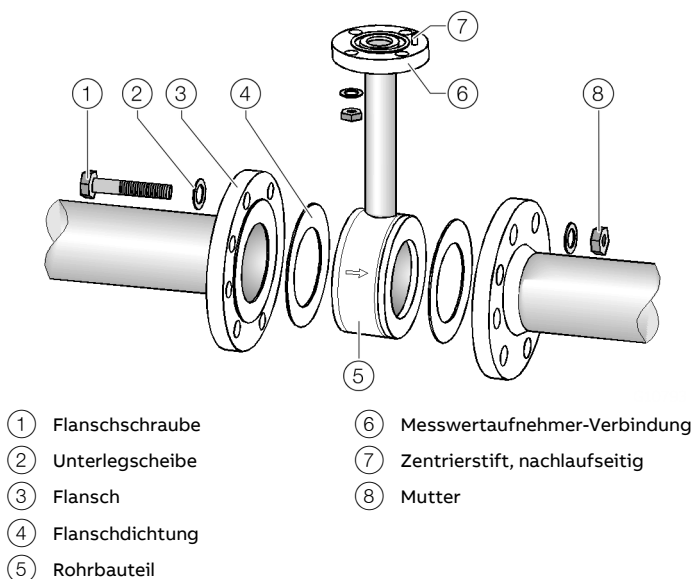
Montage Rohrbauteil (Beispiel, Zwischenflanschausführung)
